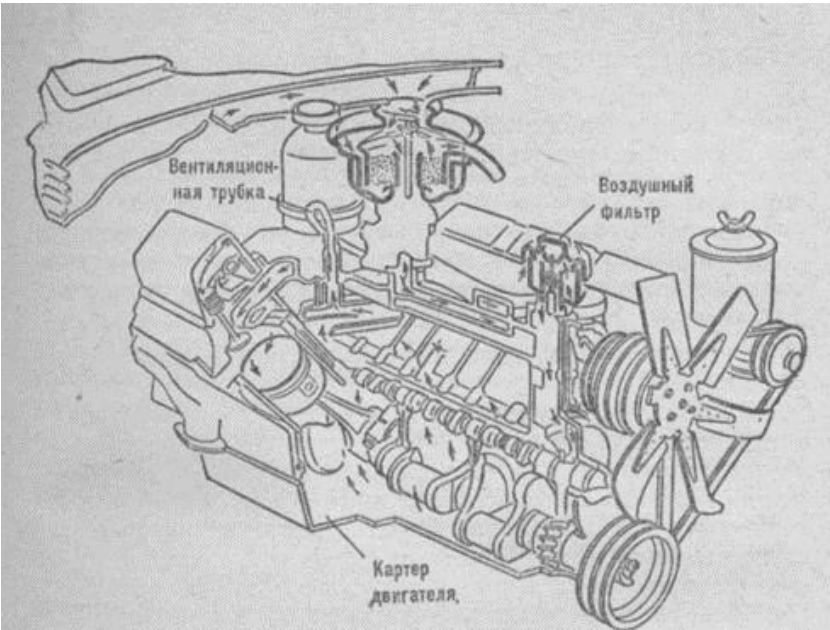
Схема вентиляции картера двигателя ЗИЛ-130
